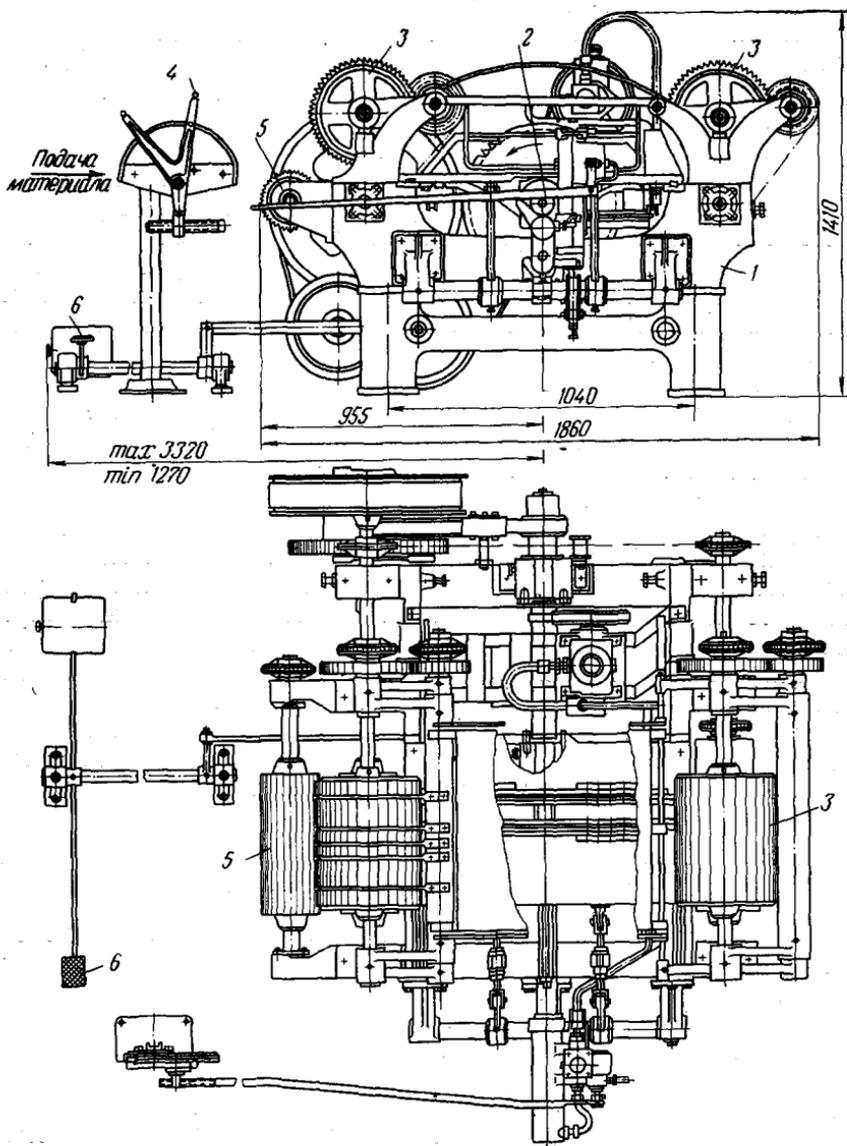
Двухпильный обрезной станок с гидроуправлением
